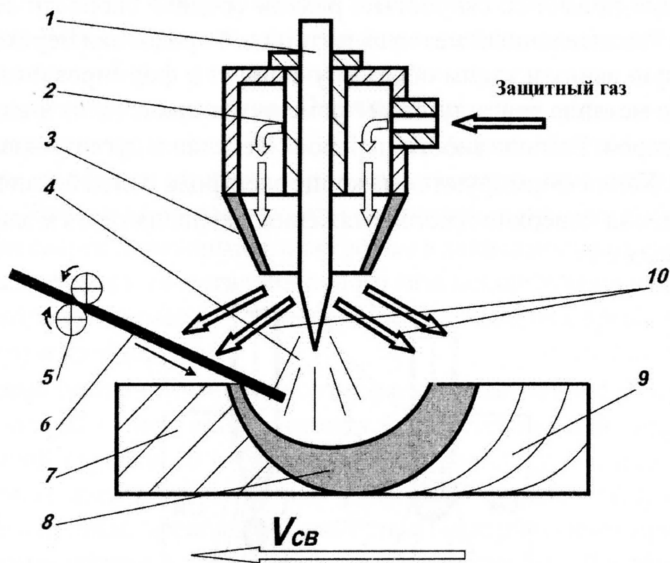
Схема технологического процесса сварки неплавящимся электродом в защитном газе:
